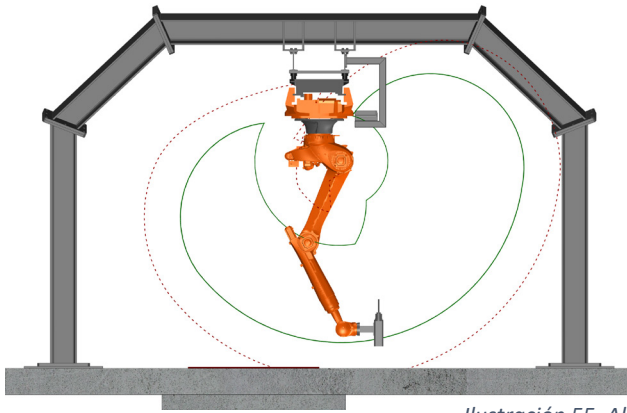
Elevación lateral laboratorio de construcción y manufactura robotizada.
